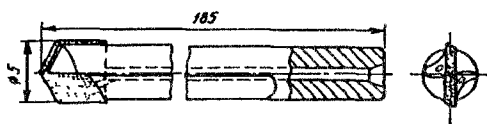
Сверло с напайкой из твердого сплава для вибросверления глубоких отверстий малого диаметра
